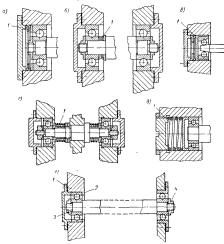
15. Схемы крепления подшипников с компенсирующими устройствами
